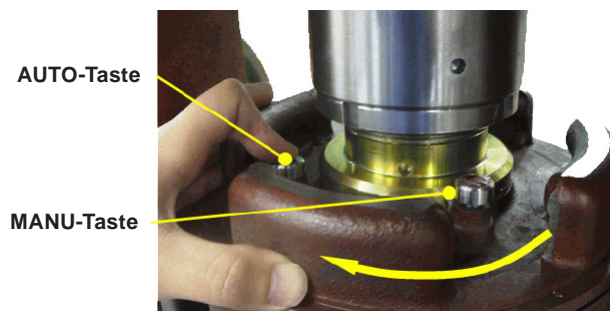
Auto-/Manu-Tasten und Kolbenschraube
